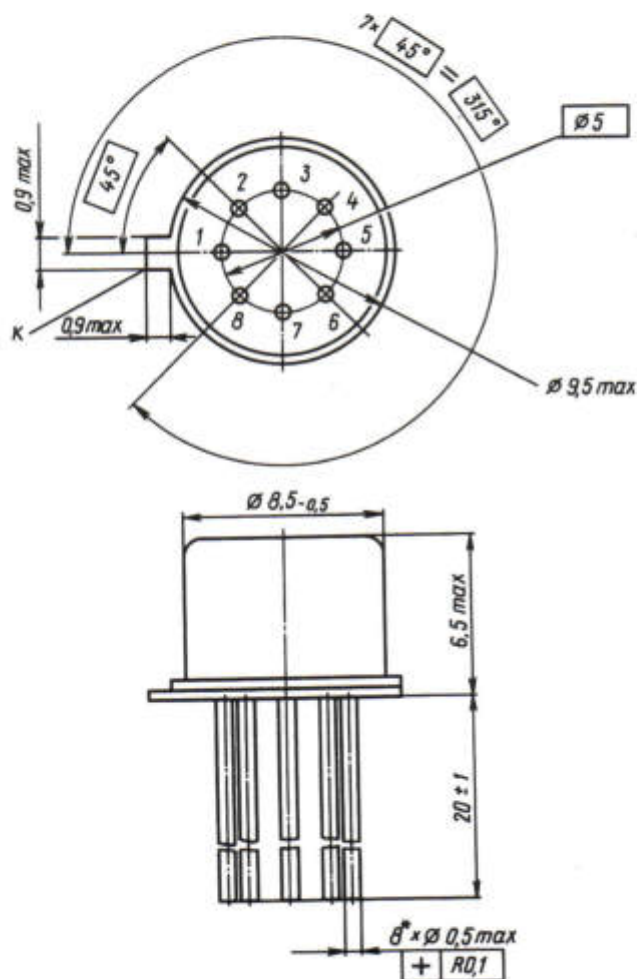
Габаритный чертеж корпуса 302.8-1 микросхем серии K544
